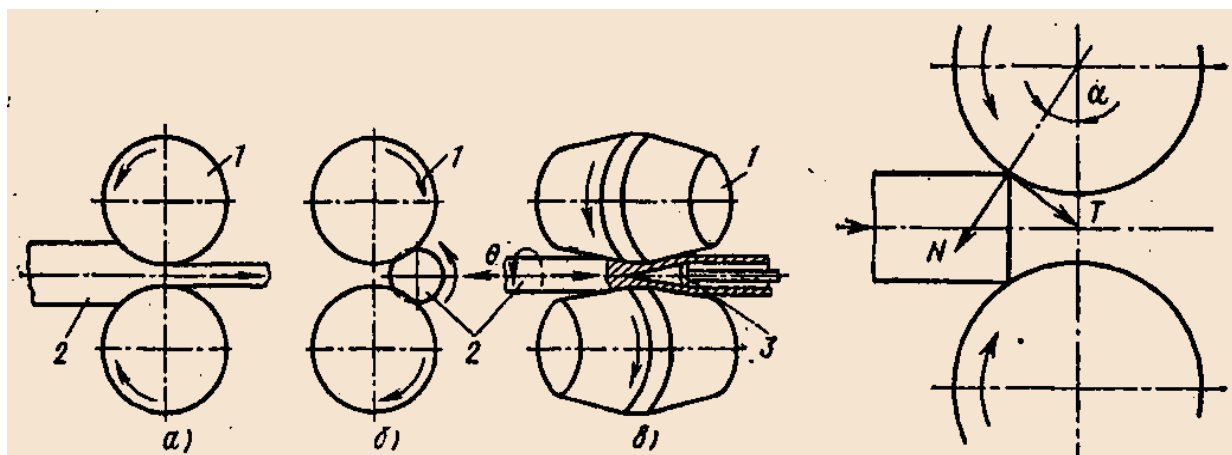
Основные виды прокатки и схема действия сил в момент захвата металла валками:
